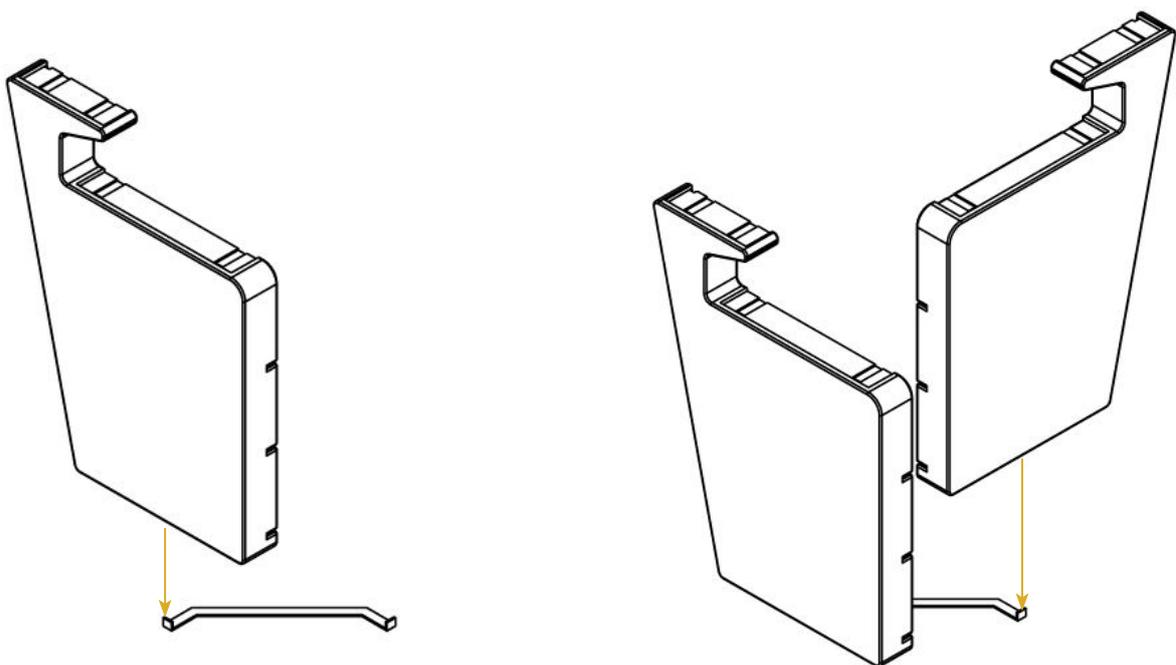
y 6-12: Paso 1 - Montaje Módulo Esquina
